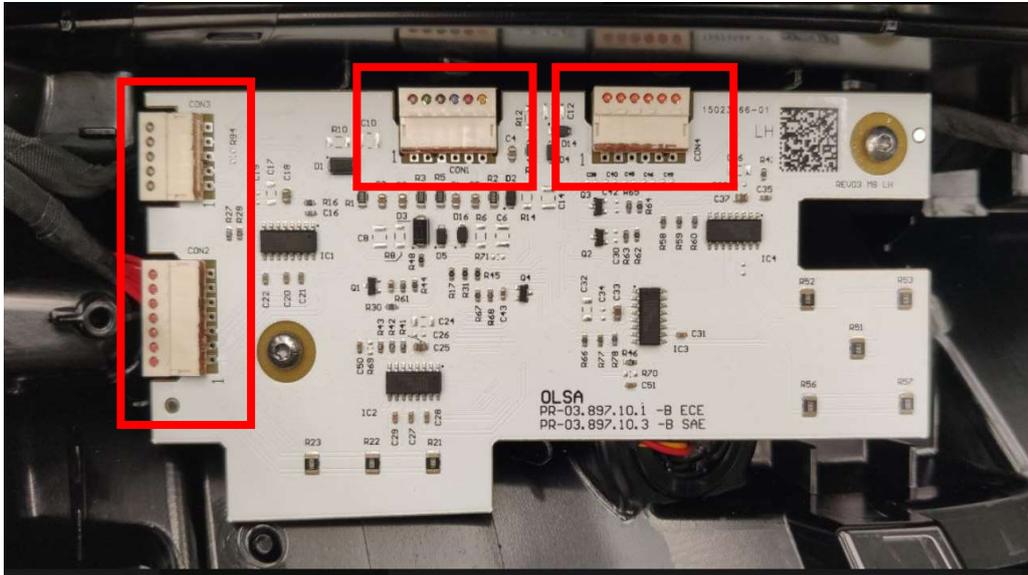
Corretto assemblaggio cablaggi nell'OP 05 per il componente T2
